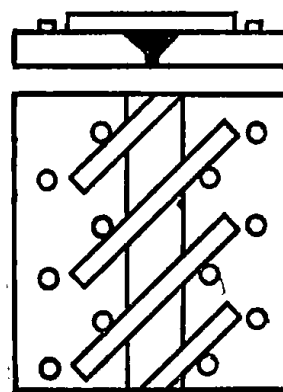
Сварка чугунных деталей при помощи шпилек и анкеров.
